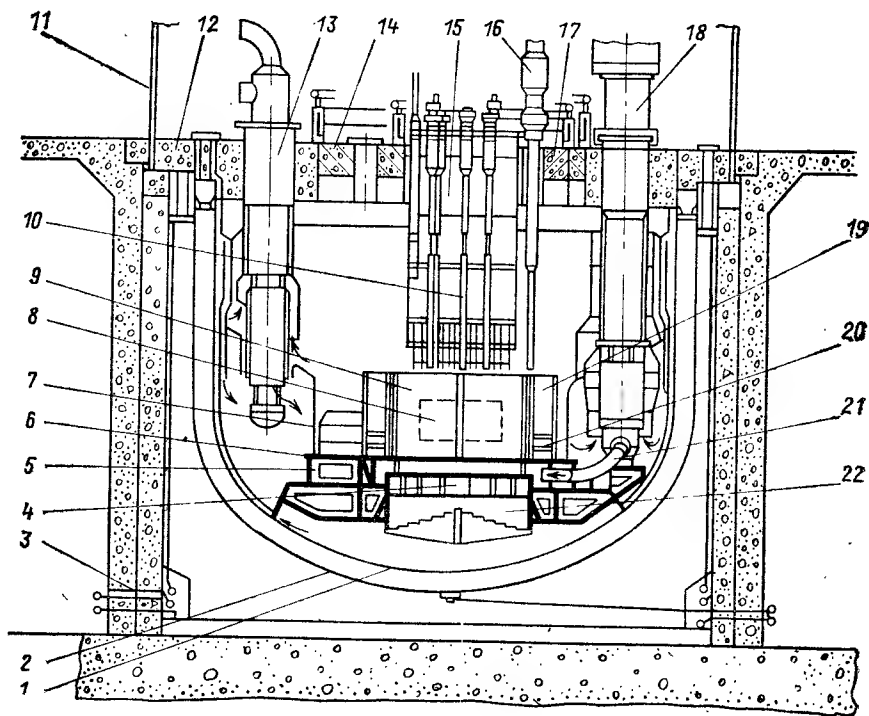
Вертикальный разрез реактора «Суперфеникс»:
